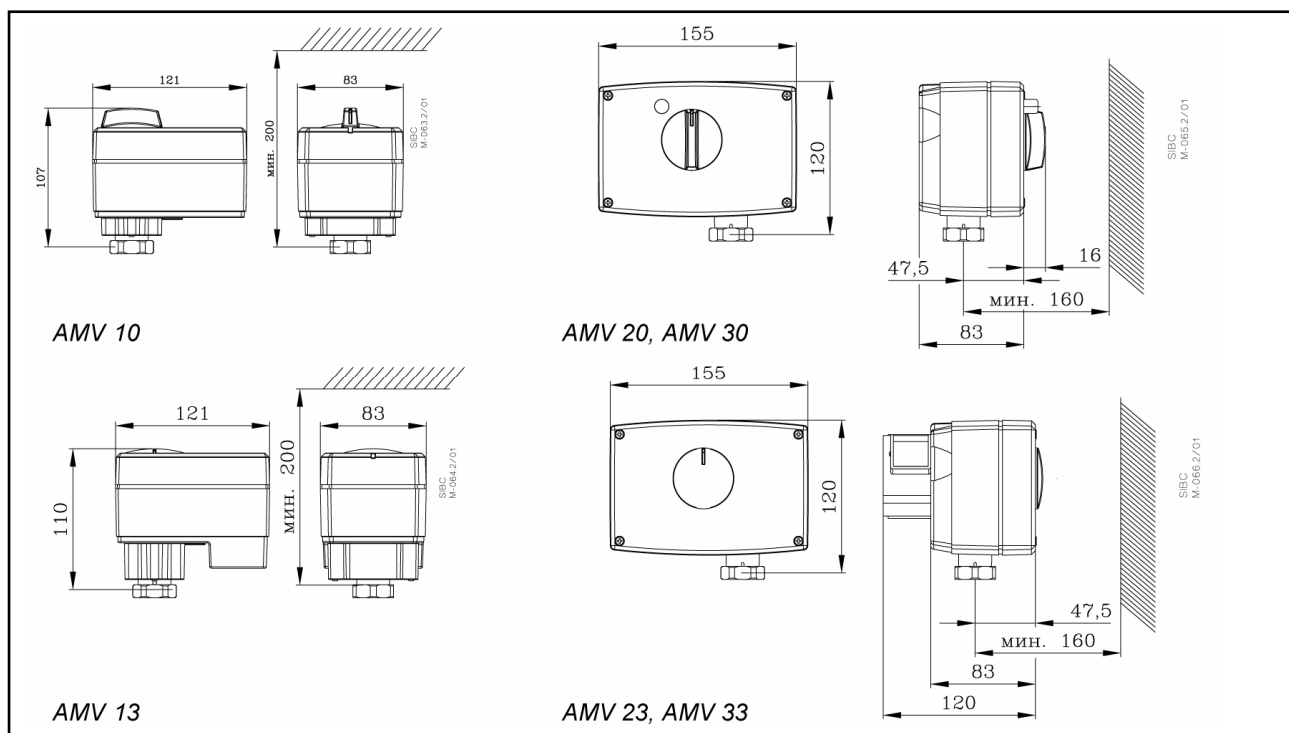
Габаритные и присоединительные размеры AMV 10, 20, 30, 13, 23, 33.
